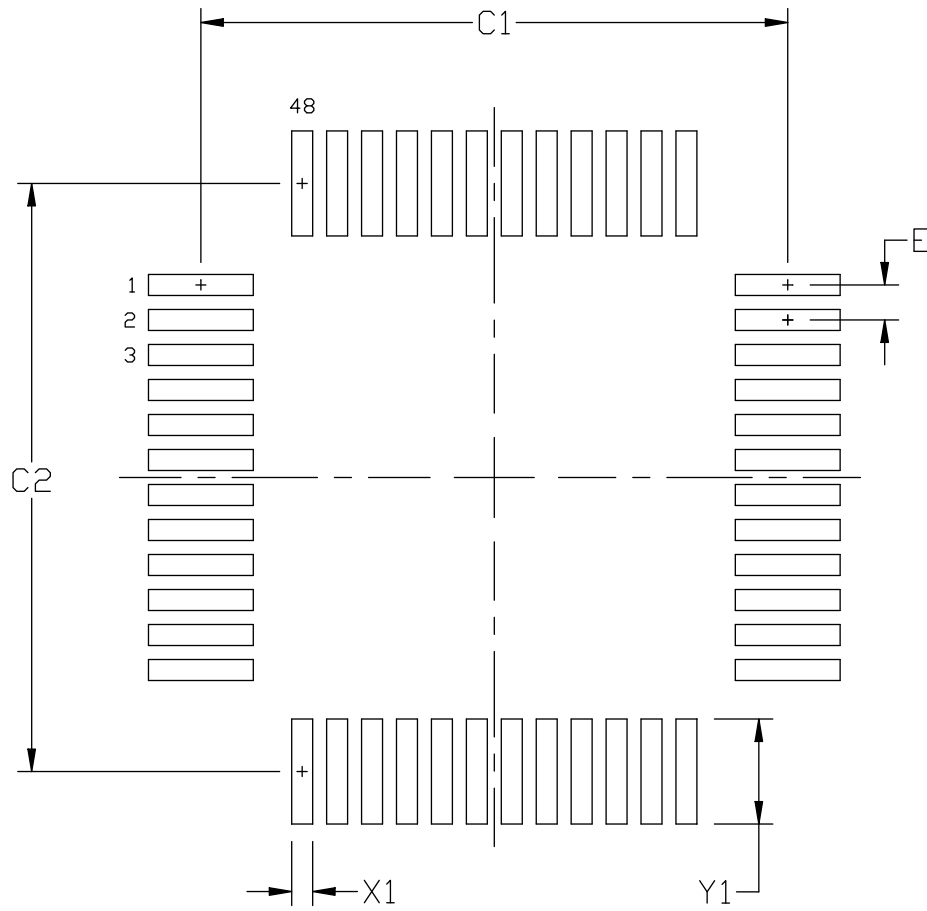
QFP48 PCB 焊盘布局图
